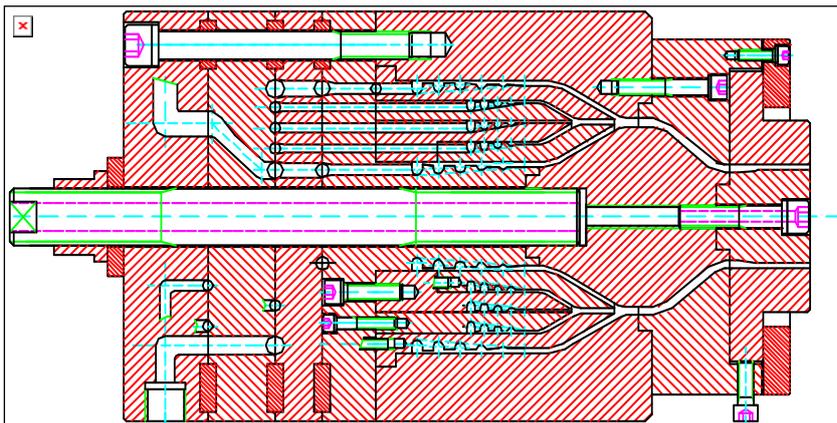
Fünfschicht-Wendelverteilerwerkzeug mit seitlicher Schmelzeinspeisung und Ringkanal-Vorverzweigung;
